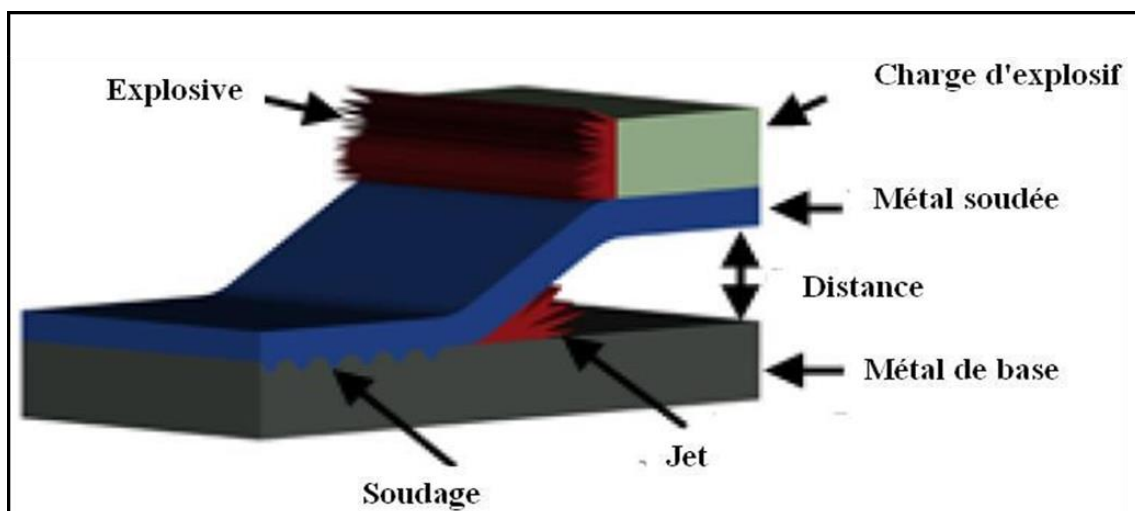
Schéma du procédé de soudage par explosion.
